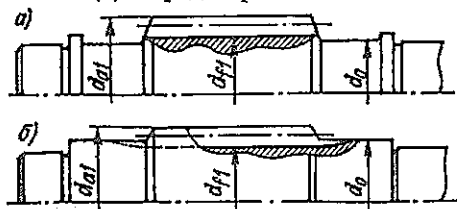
Конструкция червяка: а — при нарезании витков червяка на токарном станке; б — при фрезеровании витков червяка
